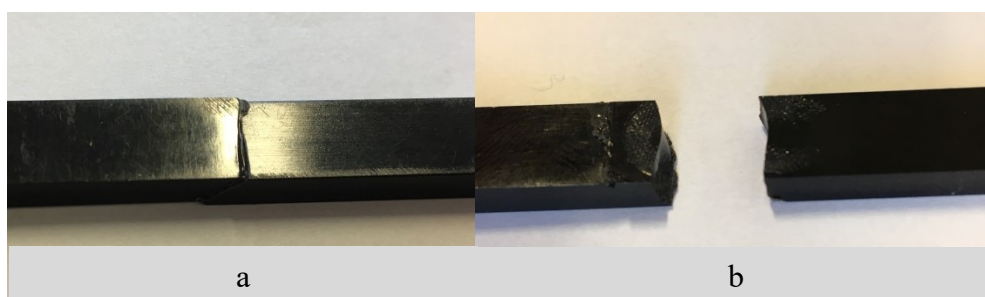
Překlátovaný spoj PC 30% R 50 J
